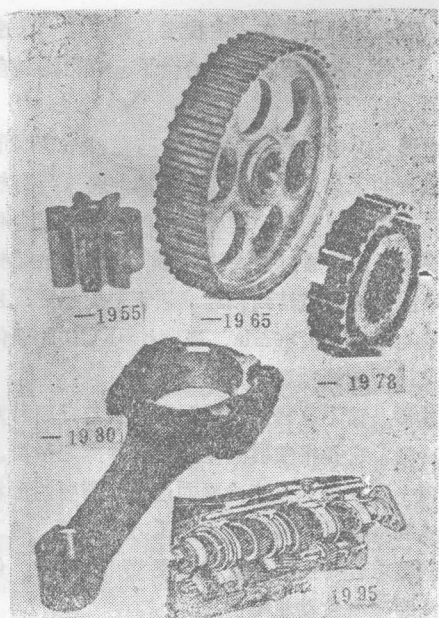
P/M结构零件在汽车发动机和齿轮箱中应用的发展情况：油泵齿轮—凸轮轴齿轮—同步衬套—连杆—承载齿轮
